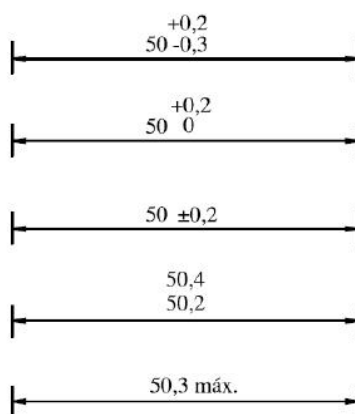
Tipos de cota para tolerancias dimensionales.
